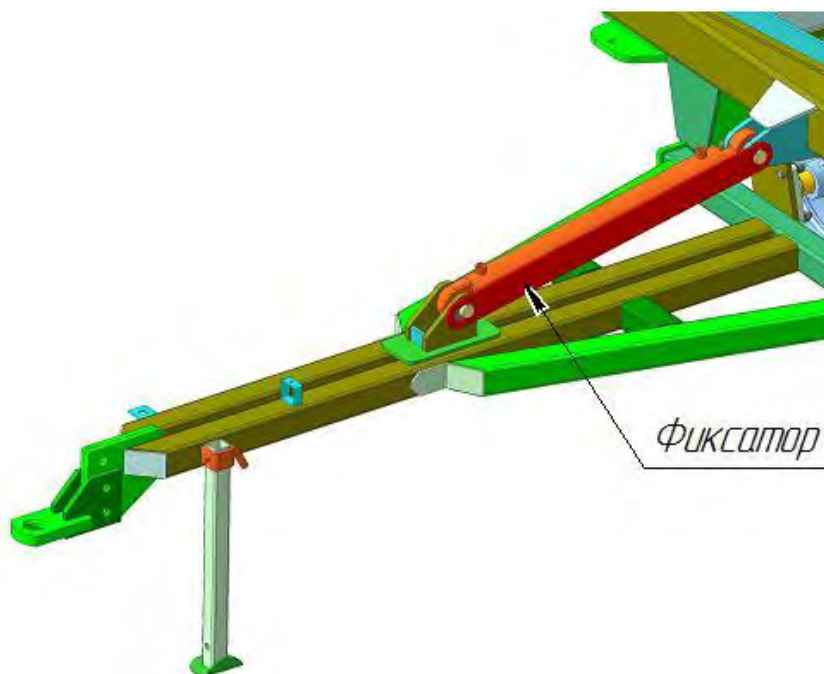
Установка фиксатора для блокировки гидроцилиндра
